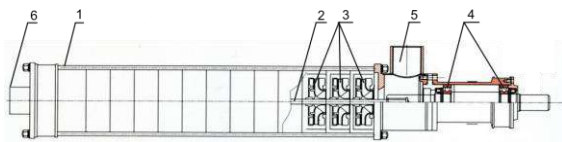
Схема насоса ЦСГ-7,2-150: 1 – корпус; 2 – вал; 3 – робочі колеса; 4 – підшипники; 5 – всмоктувальний трубопровід; 6 – нагнітальний трубопровід
